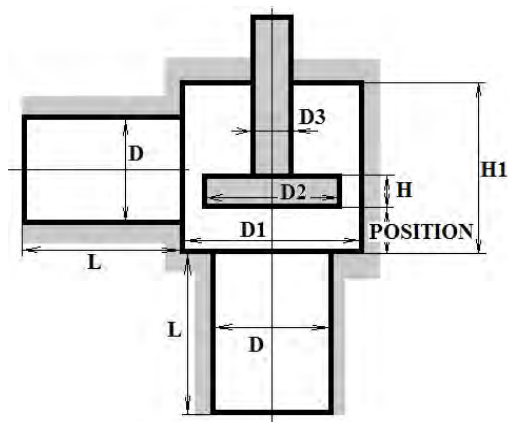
Разрез углового клапана [1; 2]. Авторский рисунок.
